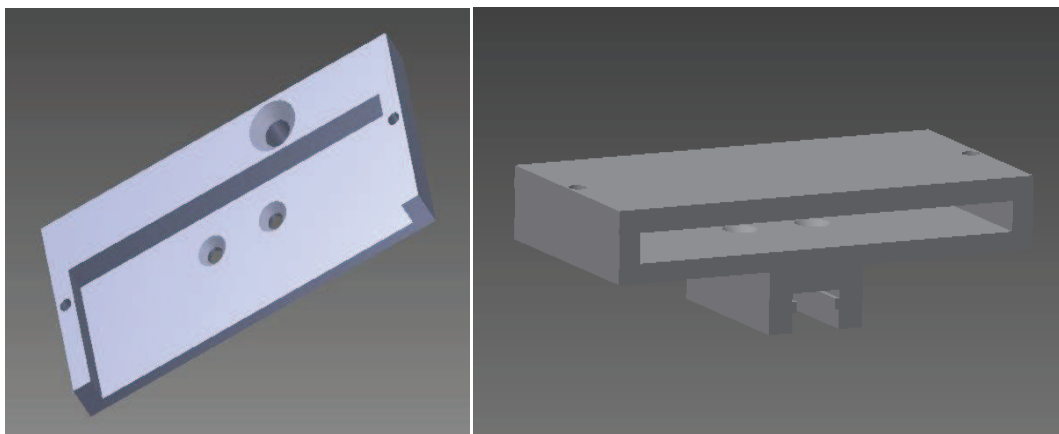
Hlavní deska přístroje s kolejnici ve 3D zobrazení: (a) deska, (b) detail
